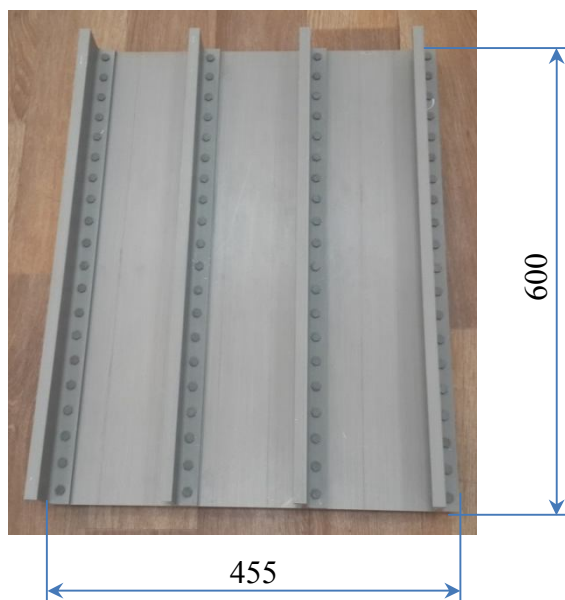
Конструктивно-подобный образец из прототипа гибридной панели крыла для испытаний на сжатие
